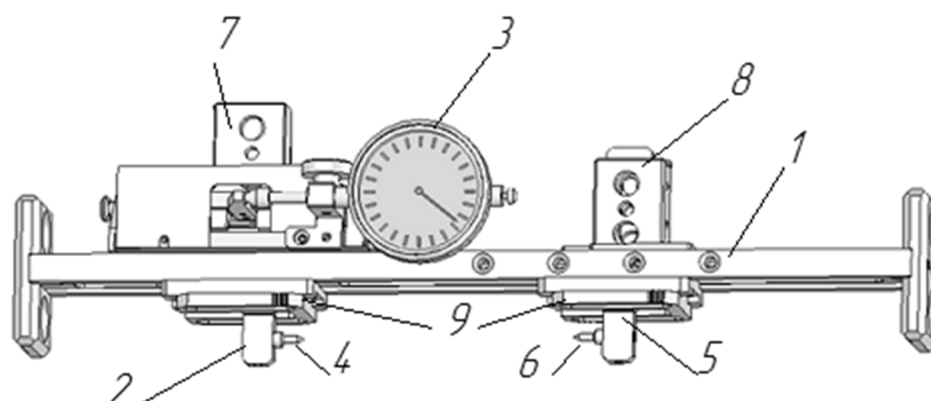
Типовая конструкция индикаторного прибора со ступенчатыми сдвижными упорами и регулируемыми по вылету штангами для измерения диаметра уплотнительной проточки трубы в измерительной плоскости и конусности уплотнительной проточки: 1 – траверса; 2 – неподвижный кронштейн; 3 – индикатор; 4, 6 – сменные
